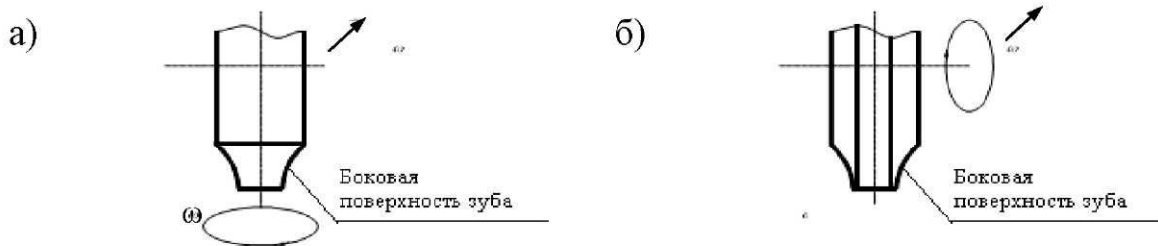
Схемы фрез для нарезания впадин зубьев:
